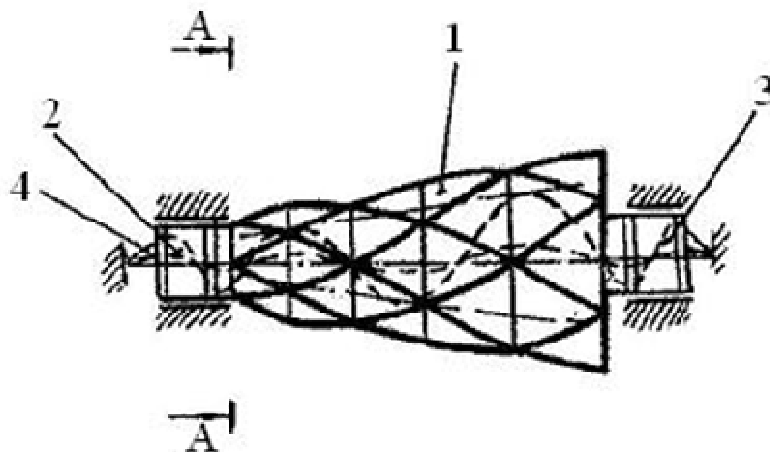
Установка для приготовления кормов в коническом винтовом барабане, вид спереди
